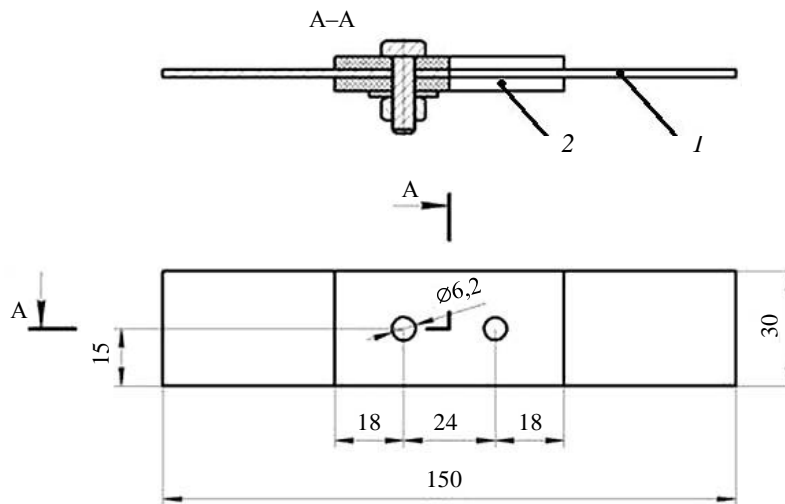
Эскиз конструктивно-подобного образца с применением двухболтового соединения для испытаний систем противокоррозионной защиты: 1 – алюминиевый сплав; 2 – углепластик
